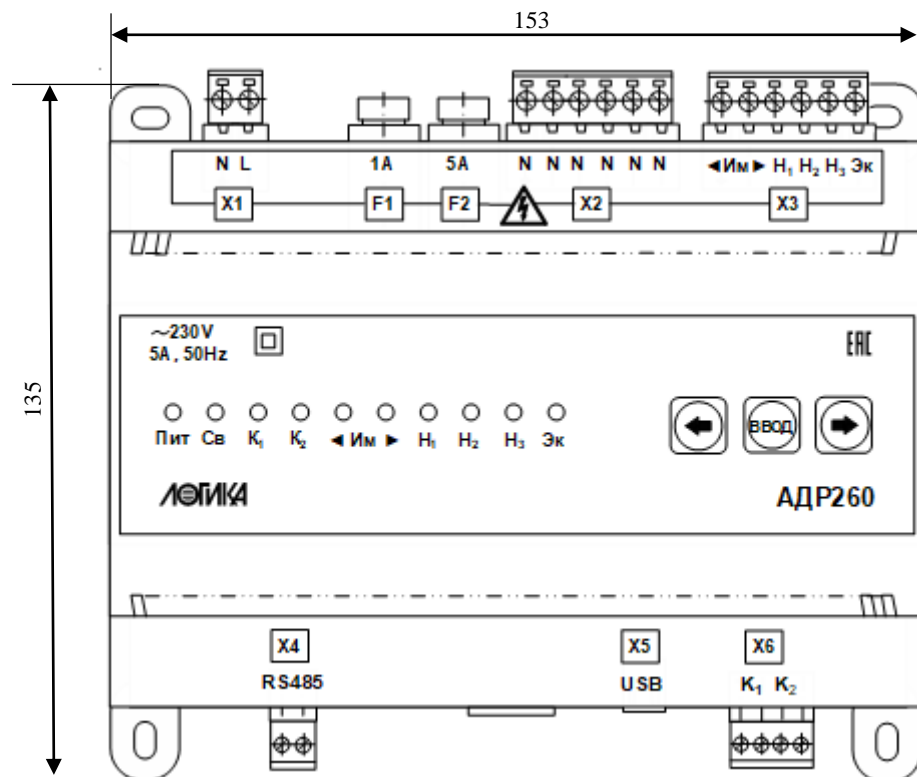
Адаптер АДР260, вид спереди, габаритные размеры.
